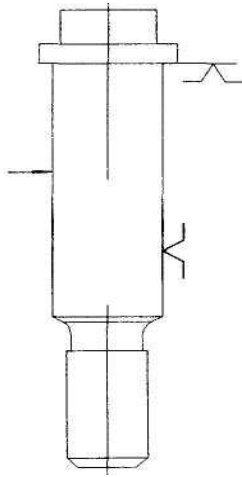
схема базування деталі в пристосуванні для фрезерування лисок
